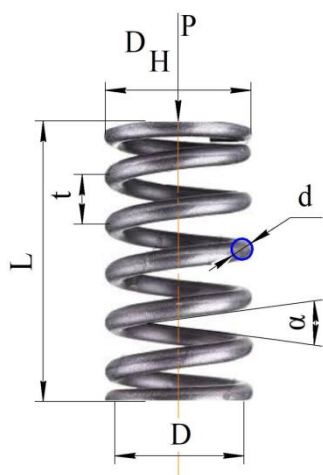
Конструкция стальной проволоочной бытовой и цилиндрической пружины
